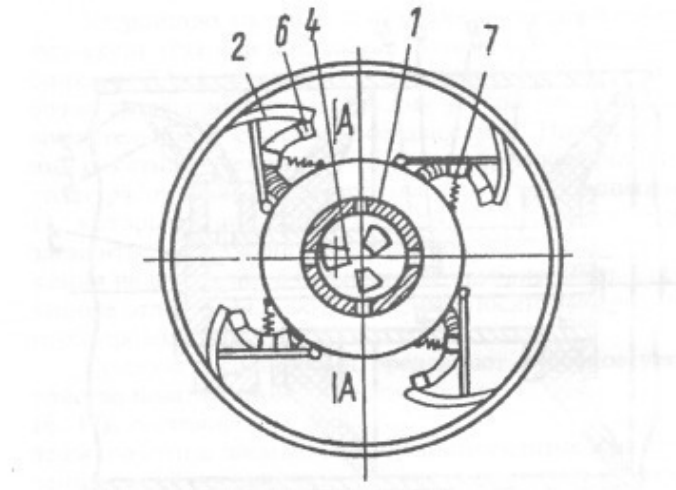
Поперечный разрез очистного устройства, где 1 – корпус; 2 – очистные элементы; 4 – перегородка; 6 – выходные сопла гидротурбинки; 7 – пружина;
